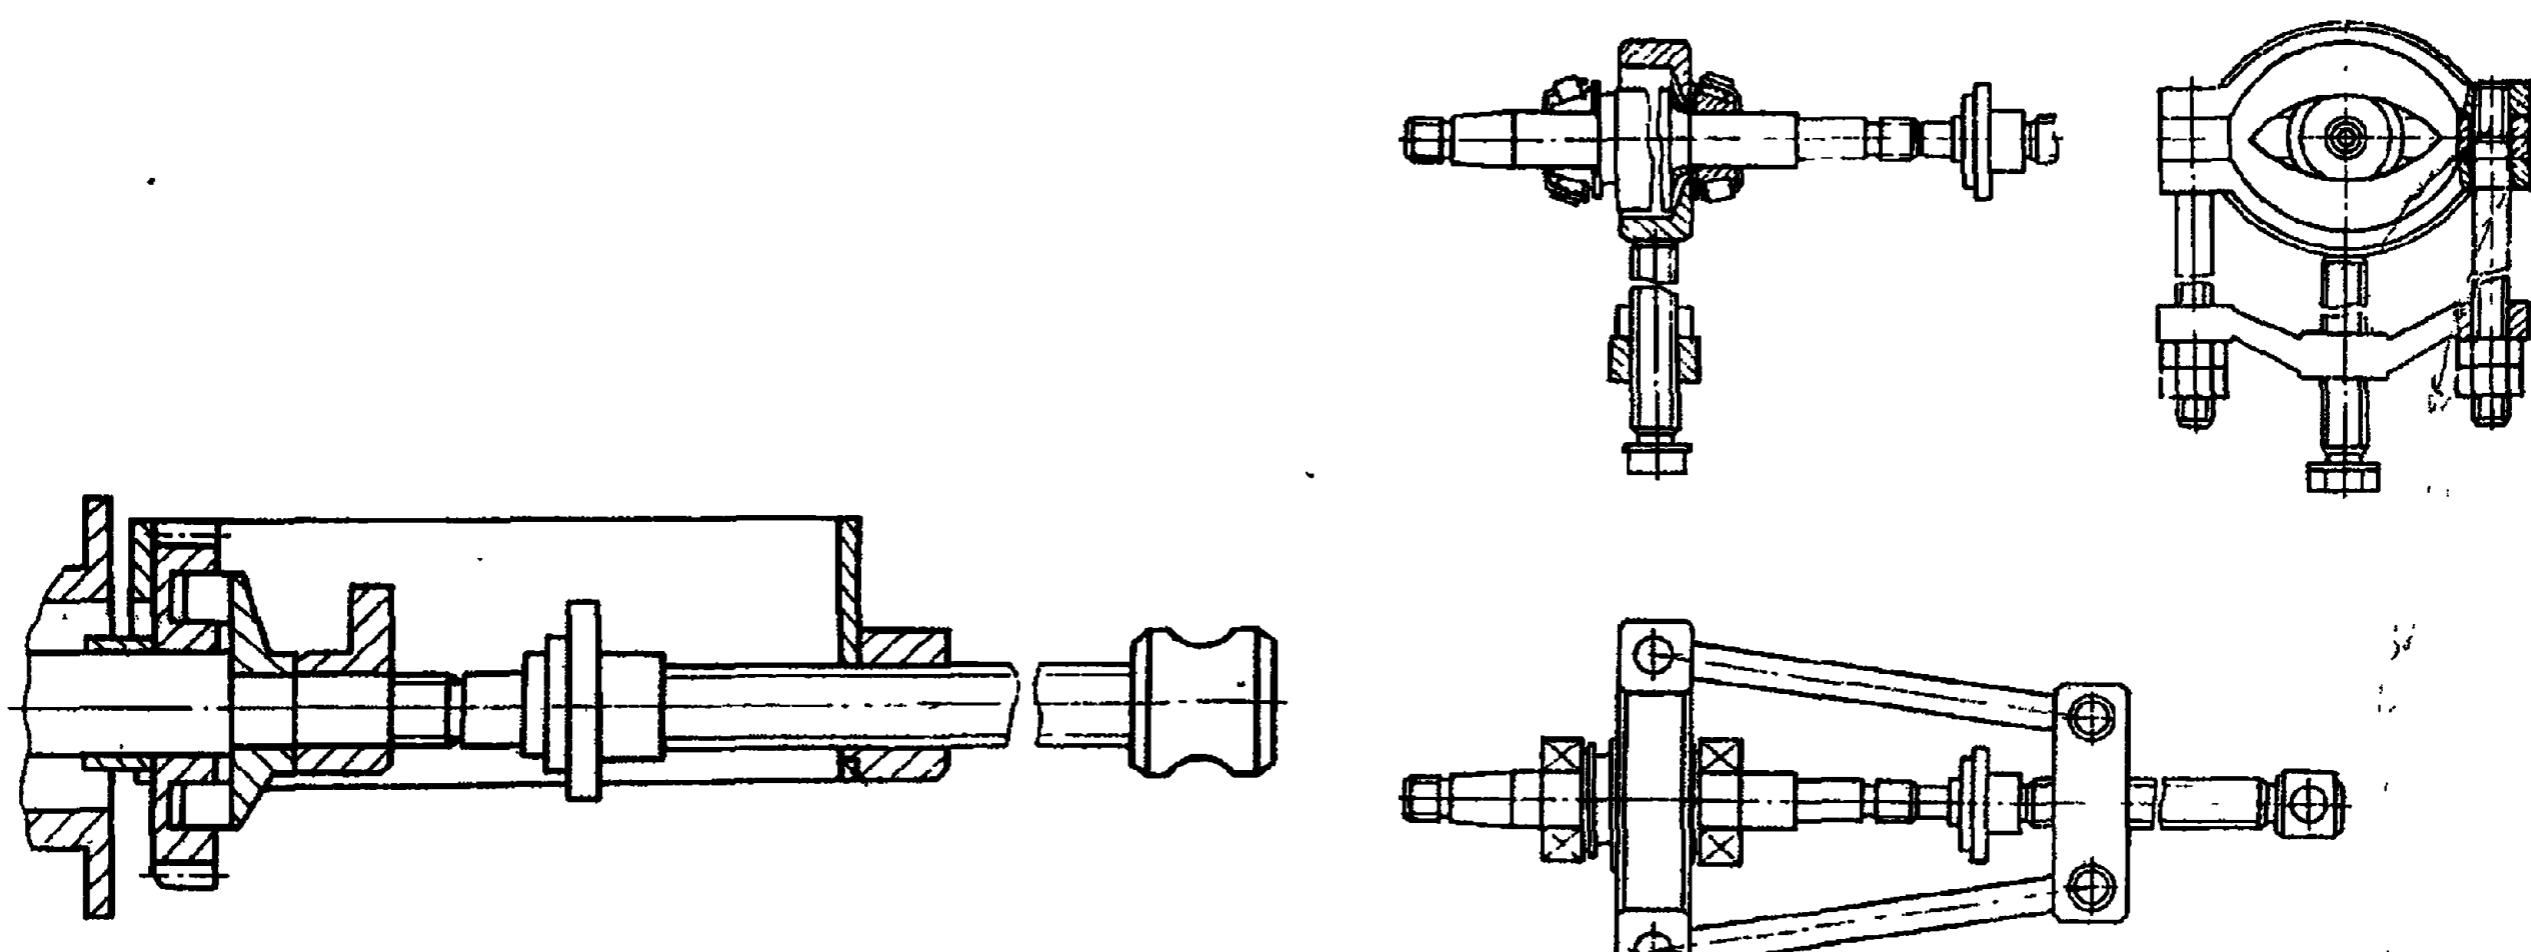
Снятие эксцентрика и ведущего зубчатого колеса с кулачкового вала ТНВД
